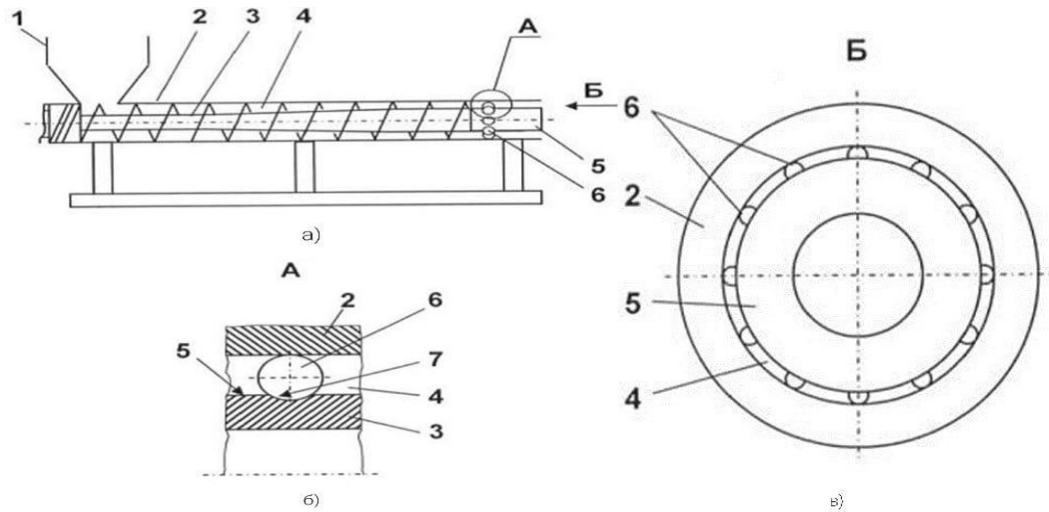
Кільцева проточка в корпусі з розміщеними в ній тілами обертання
